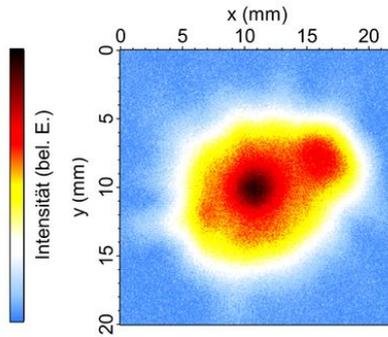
Prüfbild einer Punktschweißverbindung.
